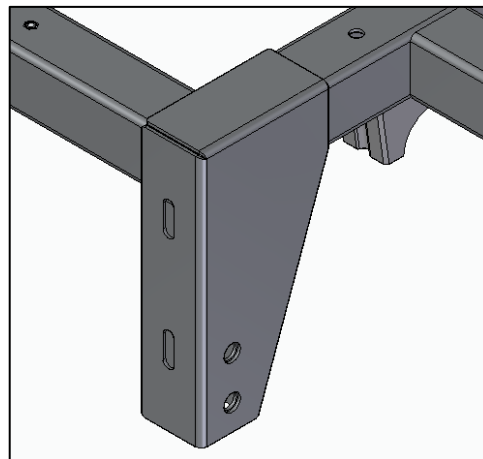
Cartela de refuerzo colocado en las bajadas de amarre de la lanza.
